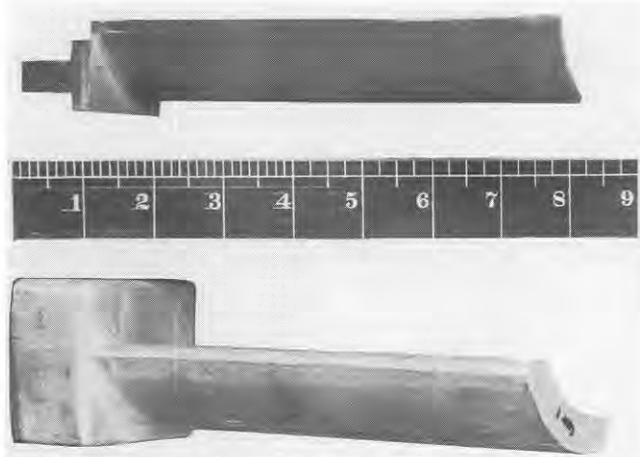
Поковка лопатки компрессора и лопатки турбины турбореактивного двигателя БМВ 109-018
